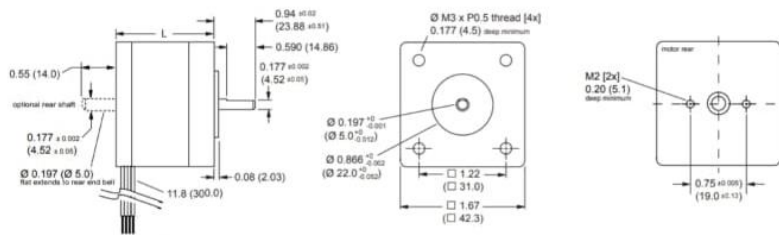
Motor de pasos Nema 17, fuente: Stepper Motors Catalogue [11].
